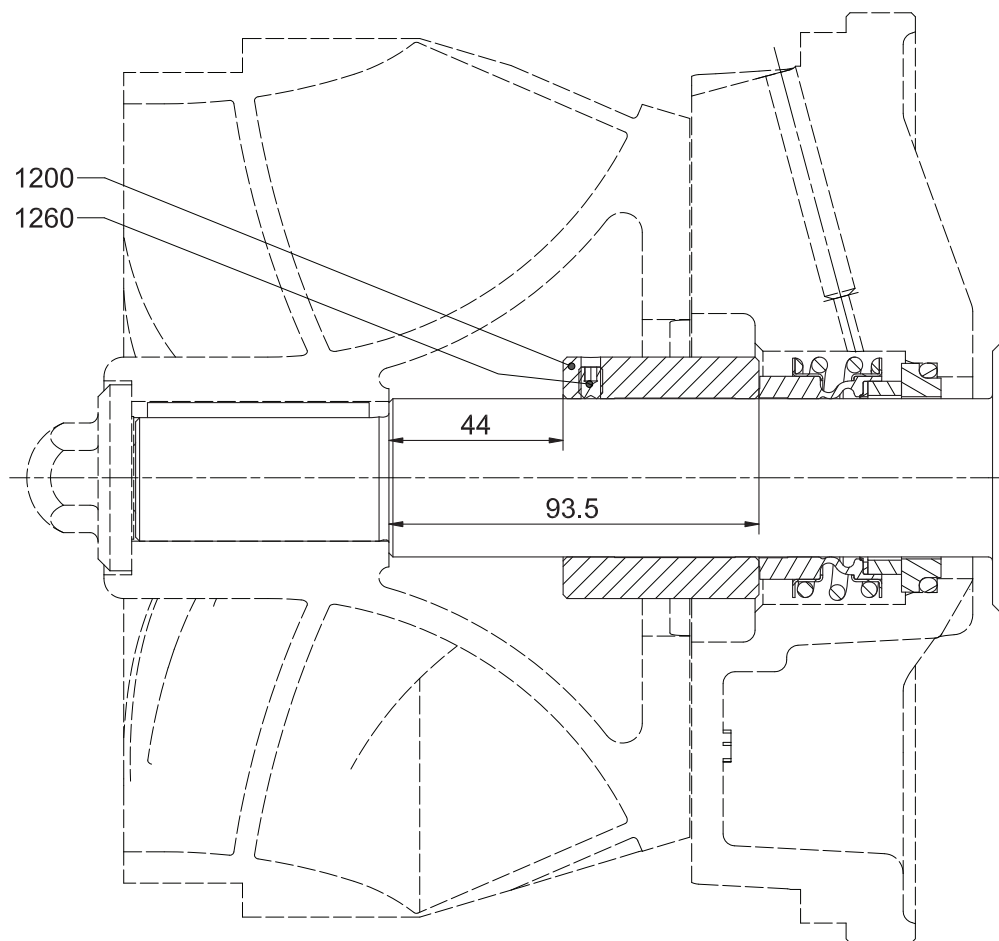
Rysunek przekrojowy 25-125, 25-160.
